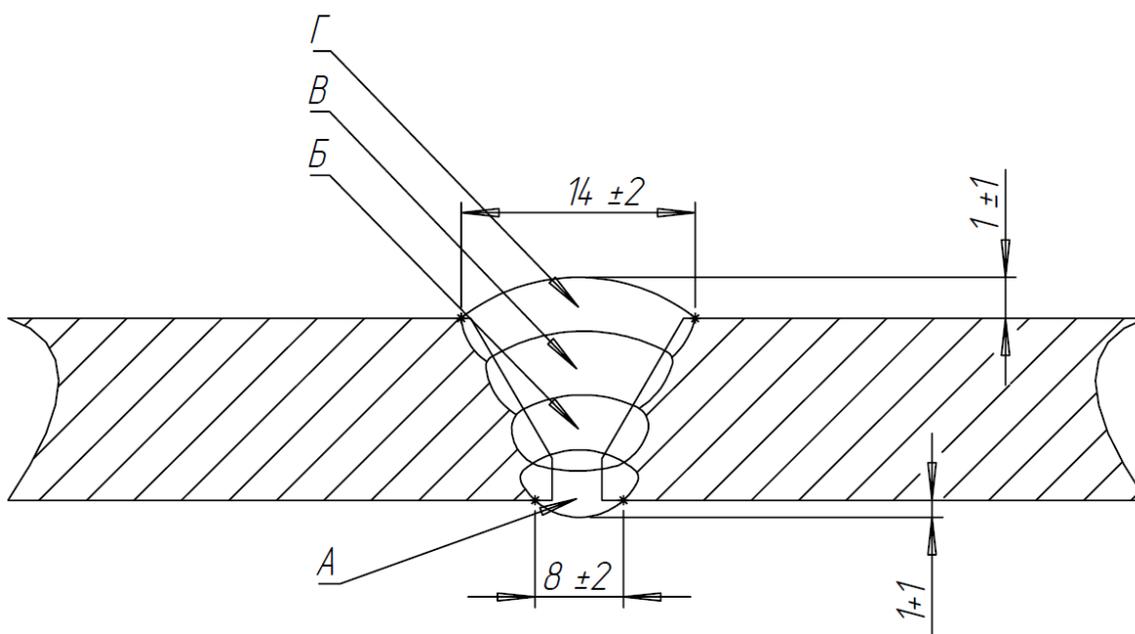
Размеры сварочного шва, согласно ГОСТ 14771-76, при толщине металла 10 мм.
